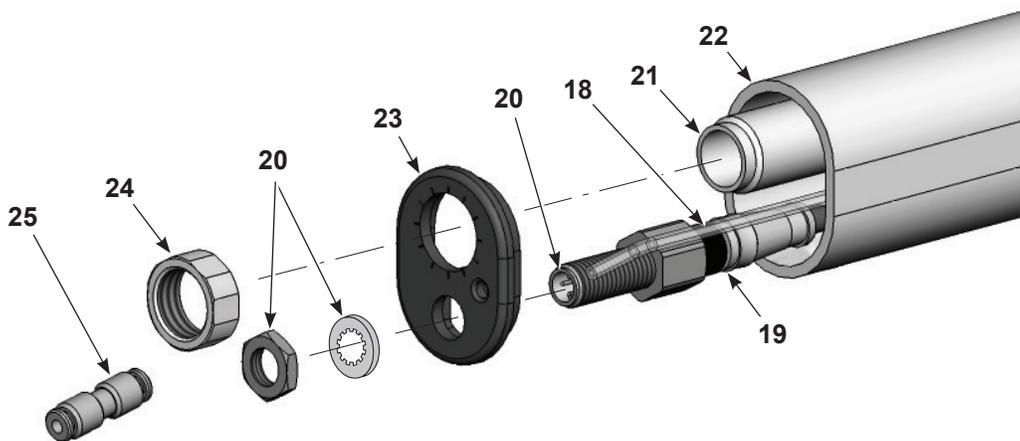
Smontaggio della pistola a spruzzo con montaggio su tubo 1 di 5
